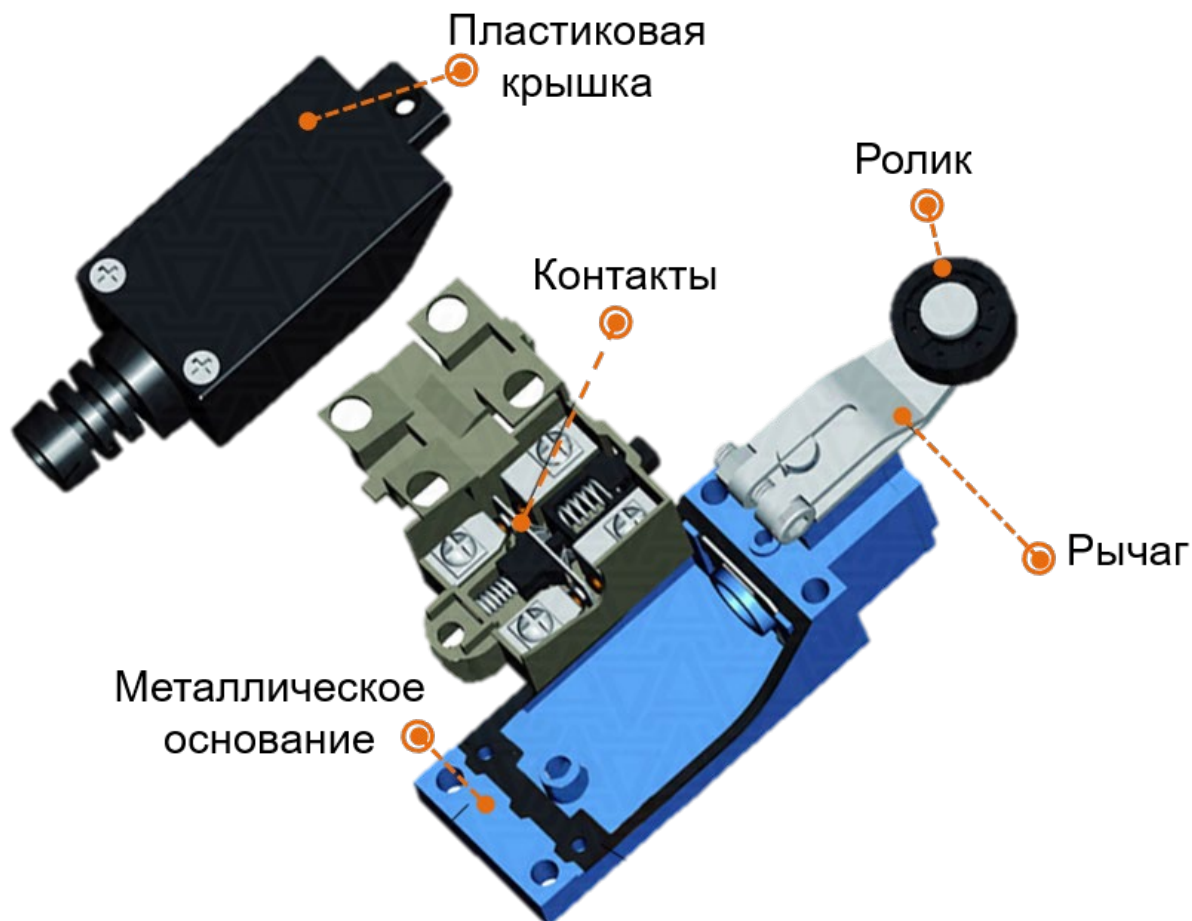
Выключатель конечной рычаг с роликом поворотный
